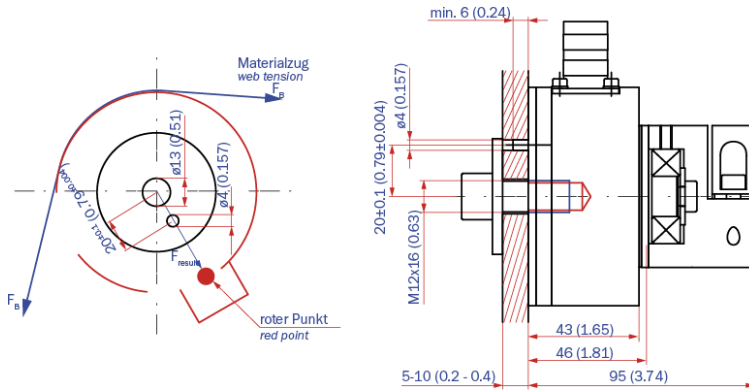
Abmessungen am Maschinenrahmen für FL Montage CA\_BA\_Manual.ai
